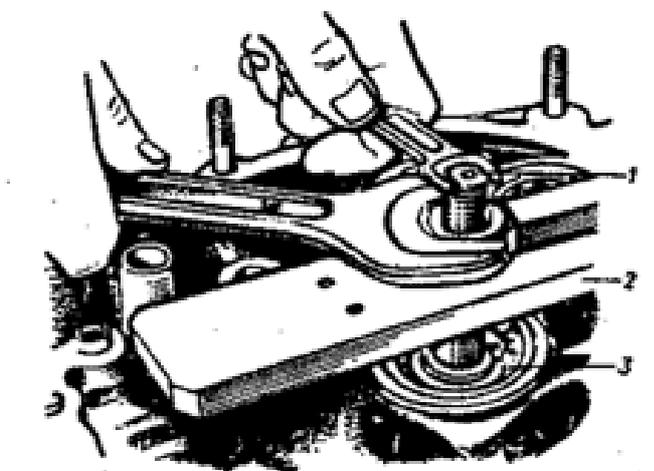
Выпрессовка роликового подшипника шестерни- вала главной передачи: 1 - болт; 2 - упор; 3 - полукольцо
